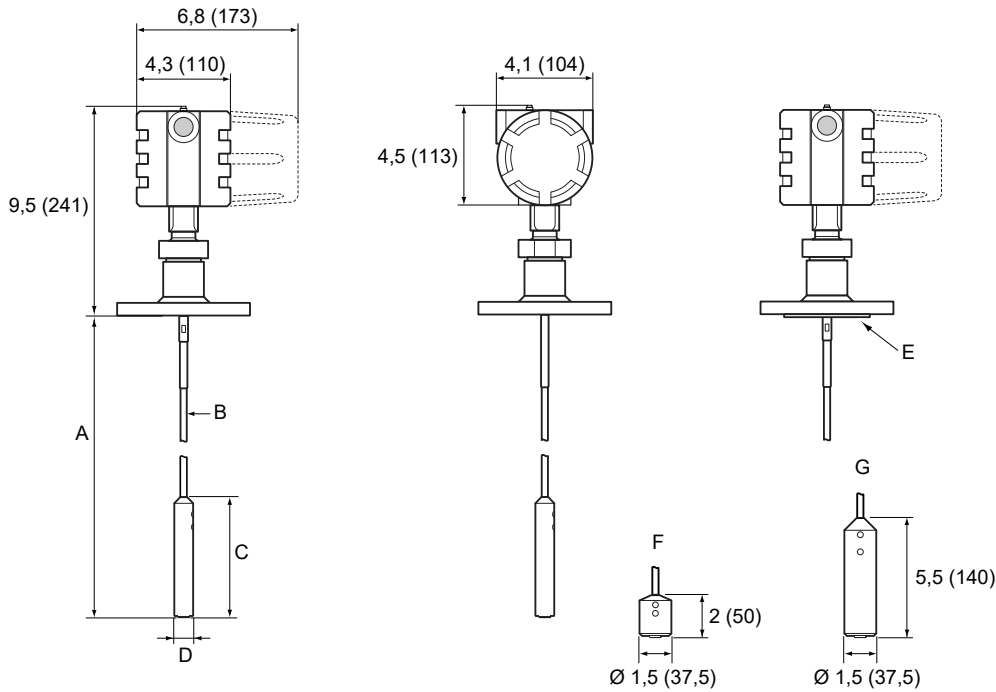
Сегментный жесткий одинарный зонд с резьбовым соединением
